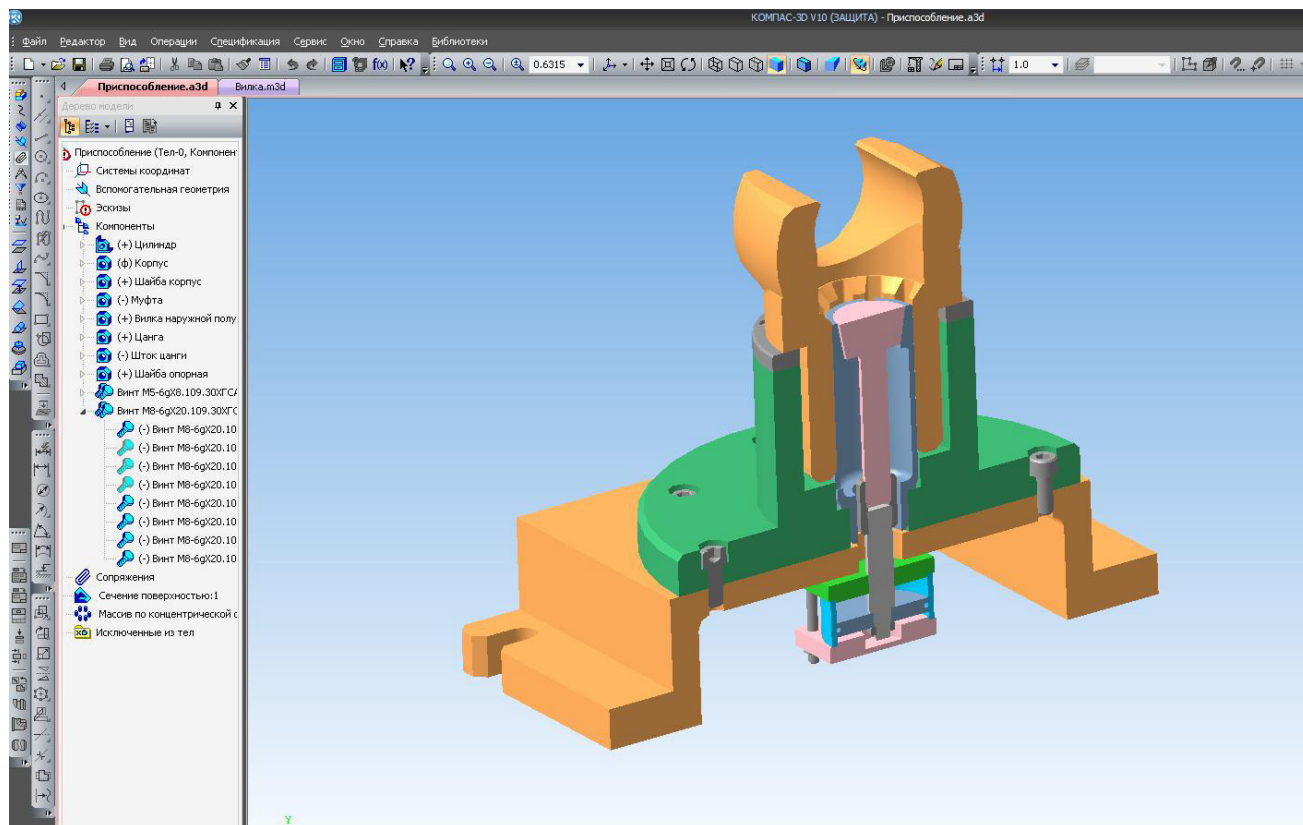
3D модель станочного приспособления в разрезе
